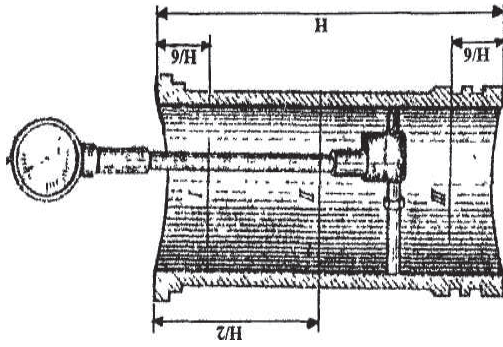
Схема измерения диаметра цилиндра блока двигателя
